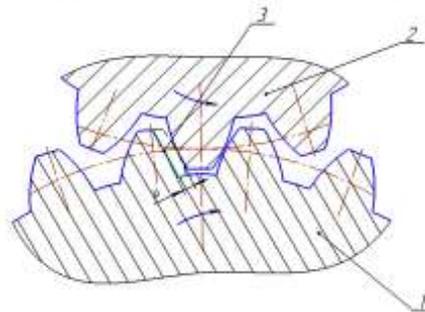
Схема зубчатого зацепления при наличии локального дефекта шестерни
